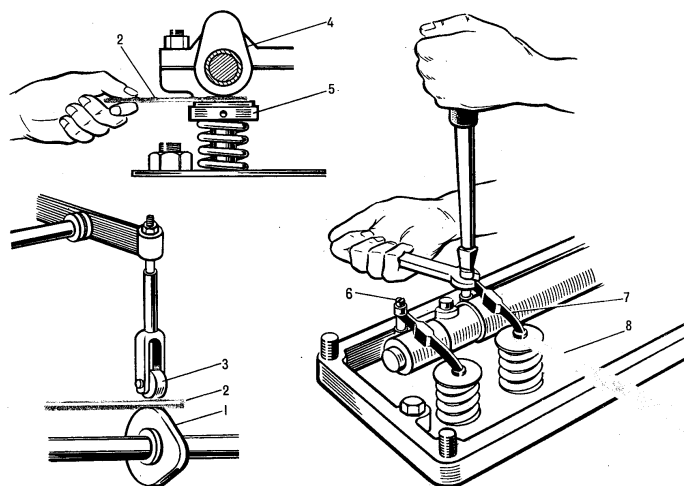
Проверка и регулировка теплового зазора в клапанном приводе где, 1-кулачная шайба, 2-измерительный щуп, 3-ролик толкателя, 4 - кулачная шайба, 5-тарелка упорная, 6-регулировочный винт, 7-клапанный рычаг, 8-щуп.
